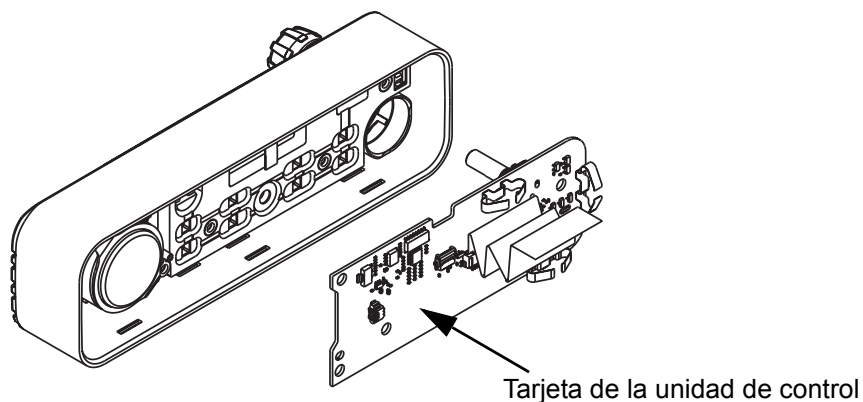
Desmontaje de la tarjeta de la unidad de control
